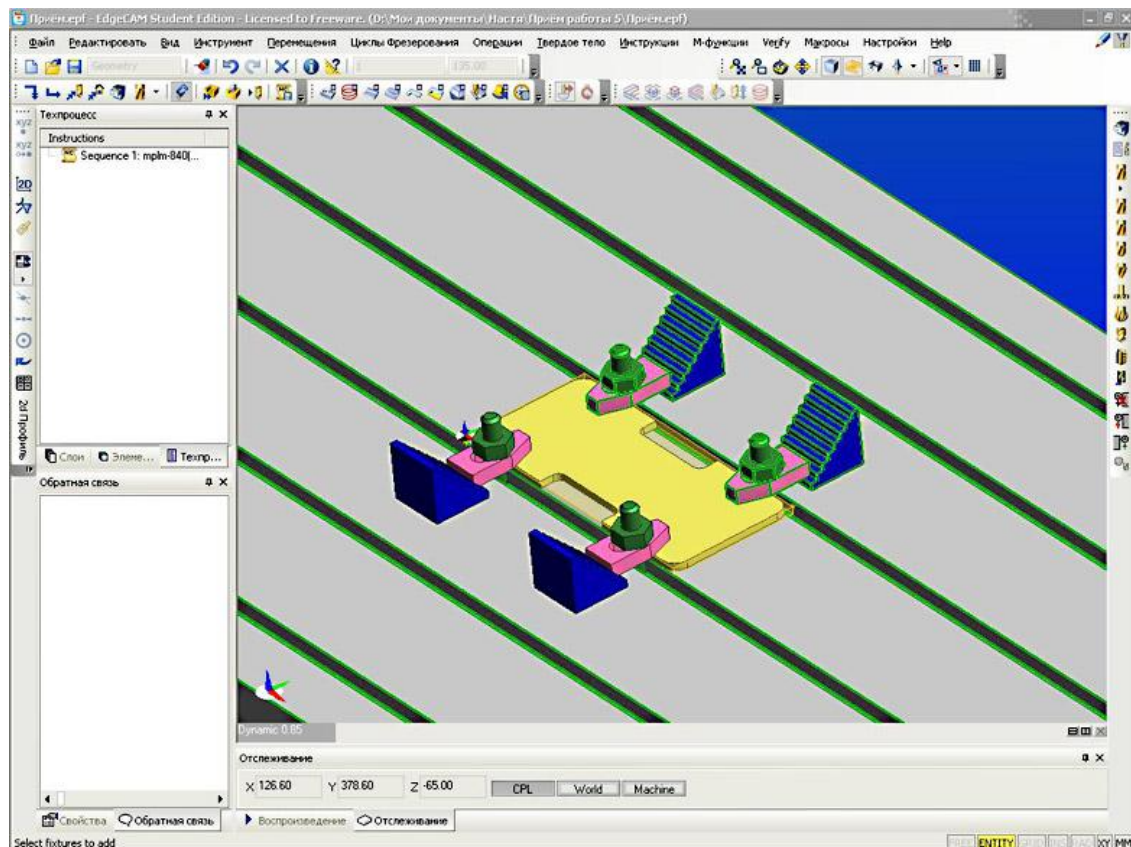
Выбрать крепёж, который будет прижимать заготовку
